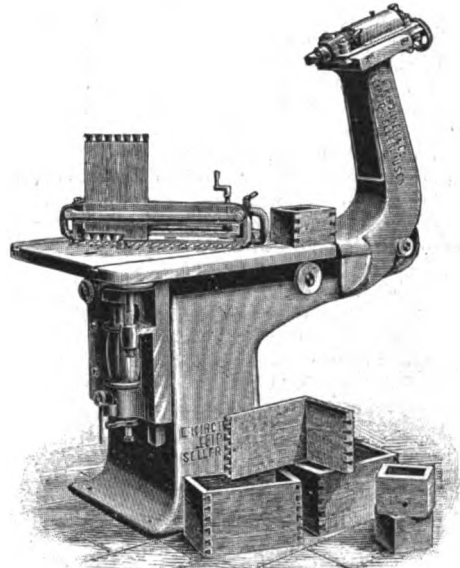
Universal-Fräsmaschine mit Zinken-Frässapparat.
